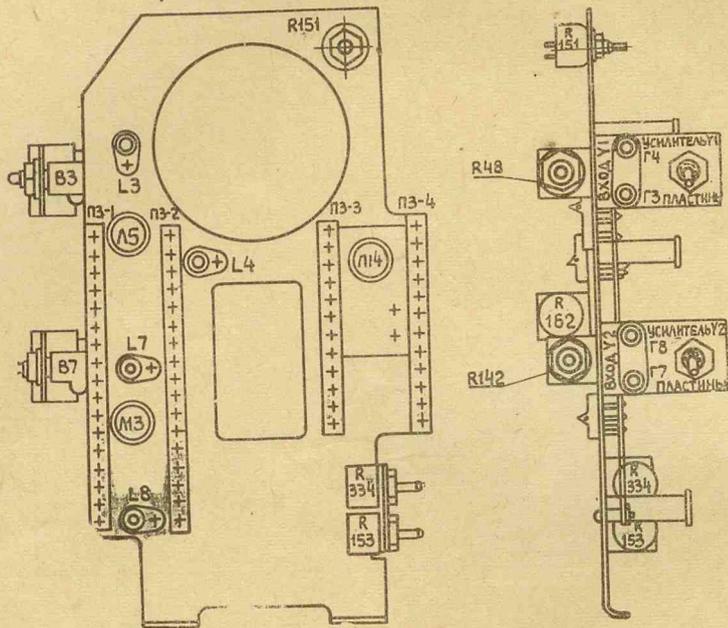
Размещение элементов на монтажных планках среднего шасси (развернуто на 90°)
